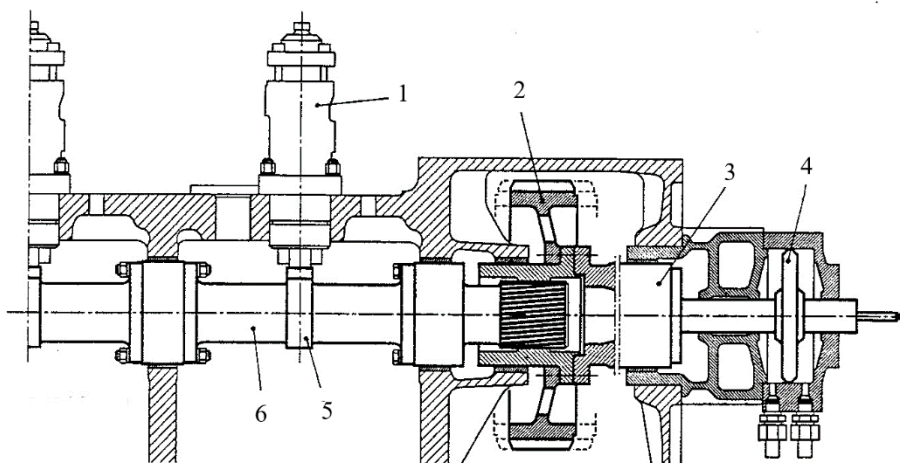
Механизм регулирования угла начала подачи топлива: 1 – топливный насос высокого давления; 2 – приводная шестерня; 3 – подшипник; 4 – гидравлический привод; 5 – топливный кулачок; 6 – распределительный вал.
